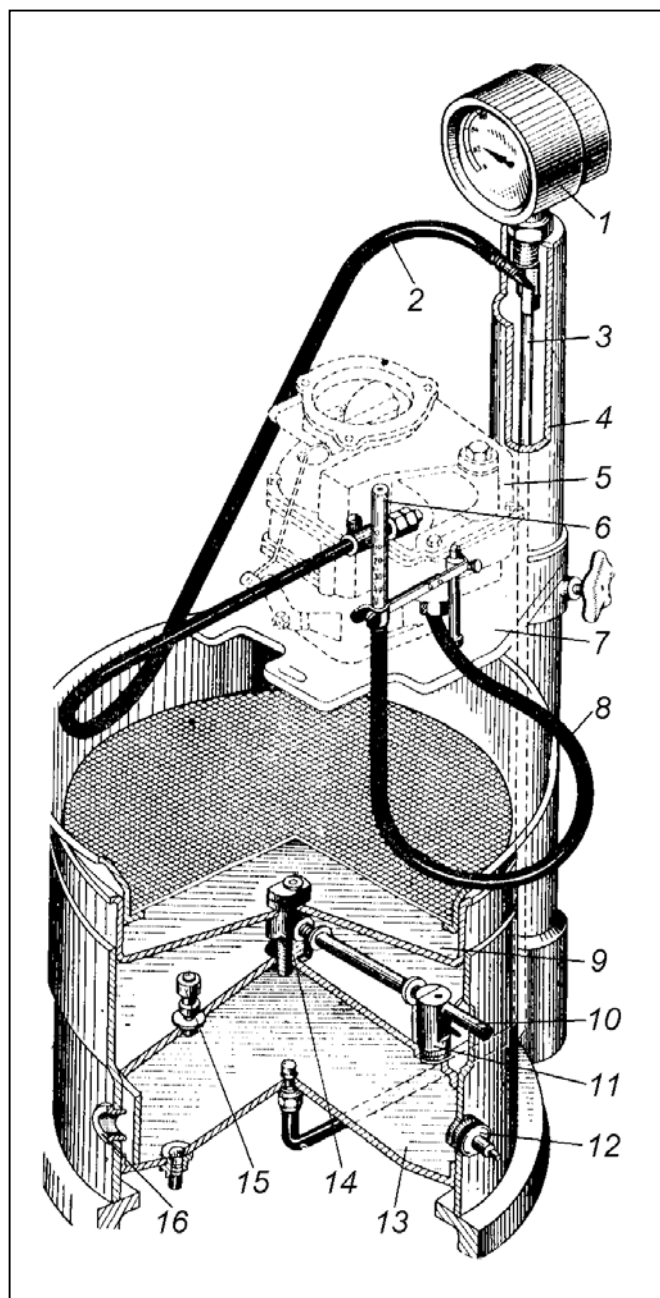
Прибор для проверки уровня топлива в поплавковой камере:
